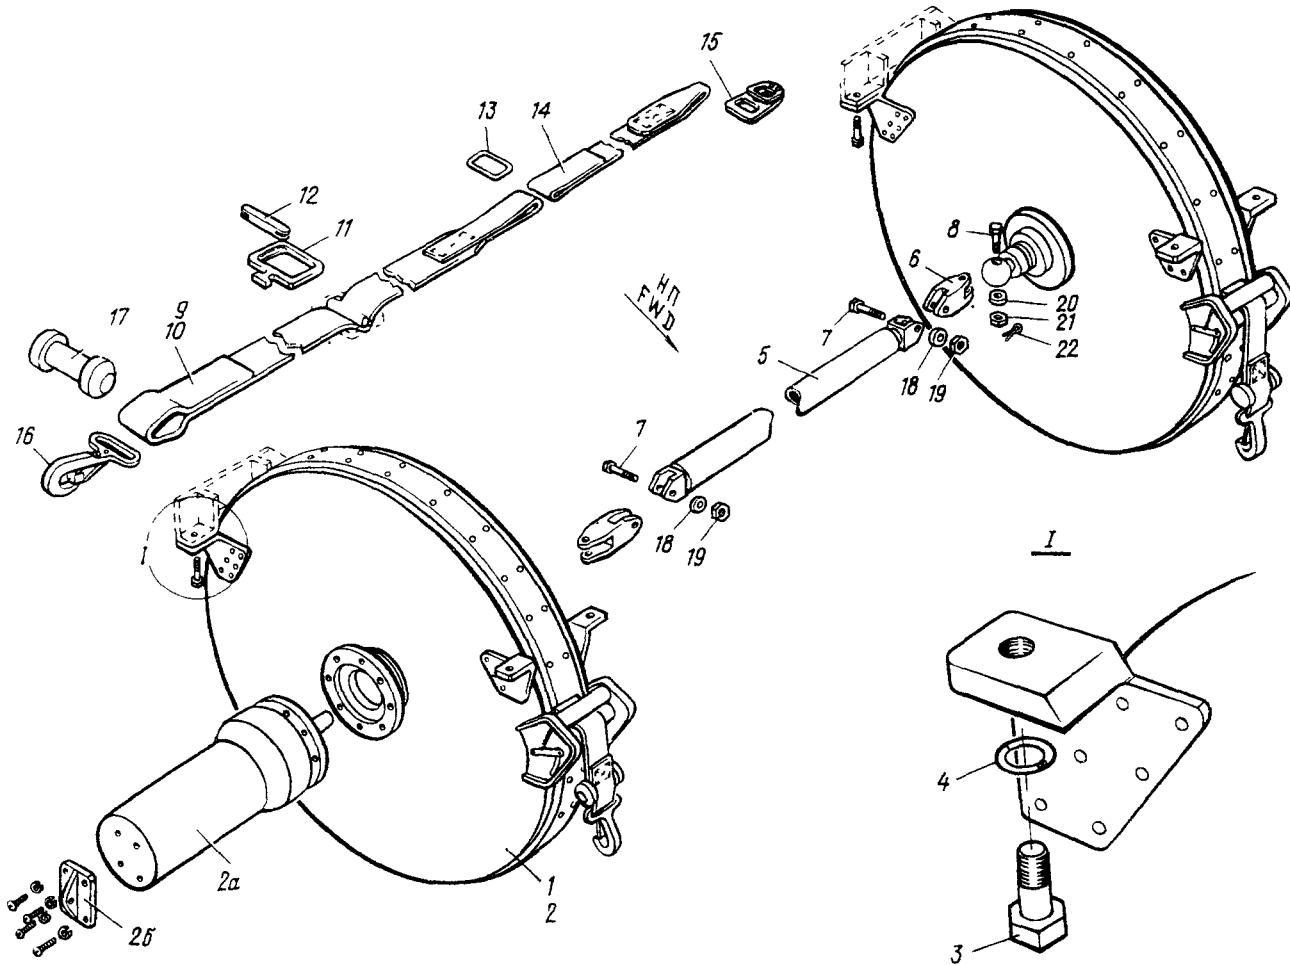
МЕХАНИЗМ УБОРКИ ШВАРТОВНЫХ ЛЯМОК
